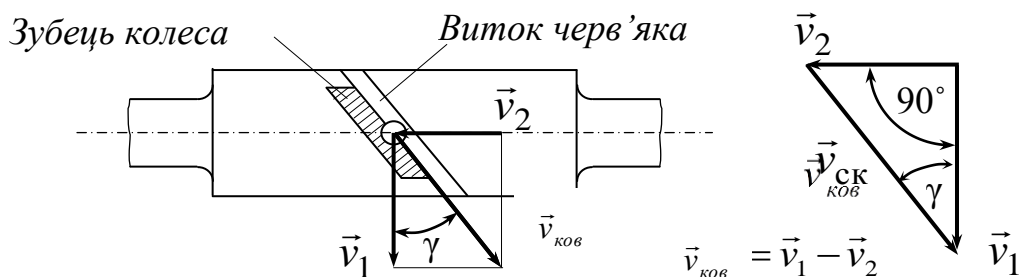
Зв'язок швидкостей в черв'ячній передачі
